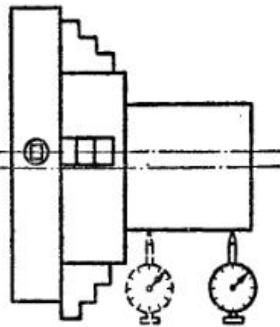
Установка эксцентриковой заготовки в четырехкулачковом патроне с выверкой по индикатору
